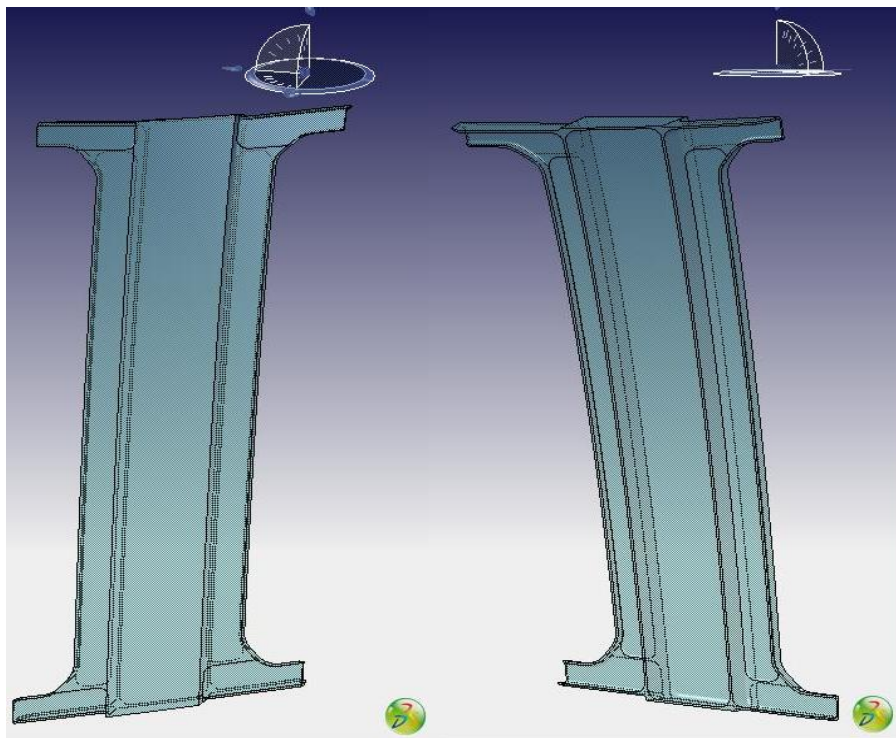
Proposta de alteração da viga lateral posterior da estrutura.
